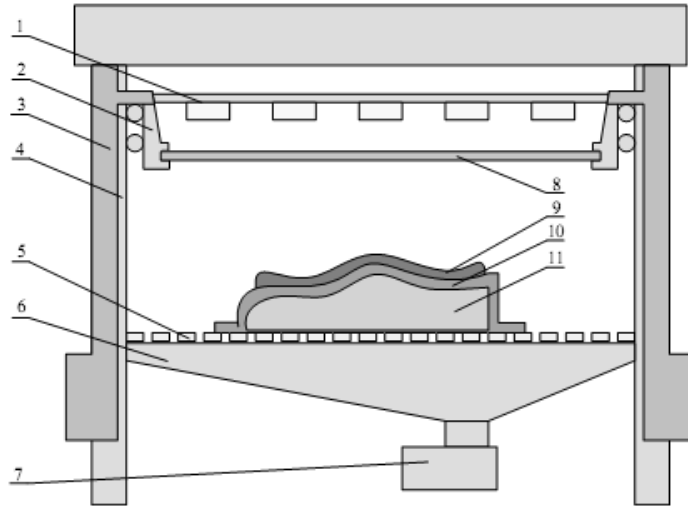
Конструктивная схема устройства для вакуумирования композитных материалов: 1 - нагревательный элемент; 2 - каретка подвижной платформы; 3 - линейный электропривод; 4 - линейные направляющие;
